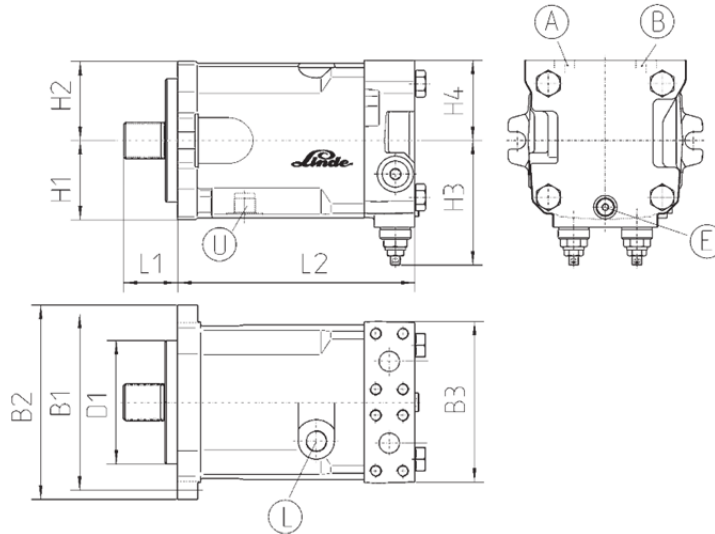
Motor hidráulico Linde Hydraulics HMF 28-02
